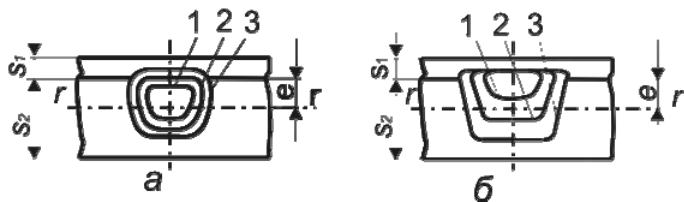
Кінетика формування ядра в деталях різної товщини ( $r-r$  – поверхня теплової рівноваги;  $e$  - відстань цієї поверхні від зварювального контакту): *a* - м'який, *б* - жорсткий режими зварювання; 1-3 - ізотерми плавлення на початку, посередині та в кінці зварювання
